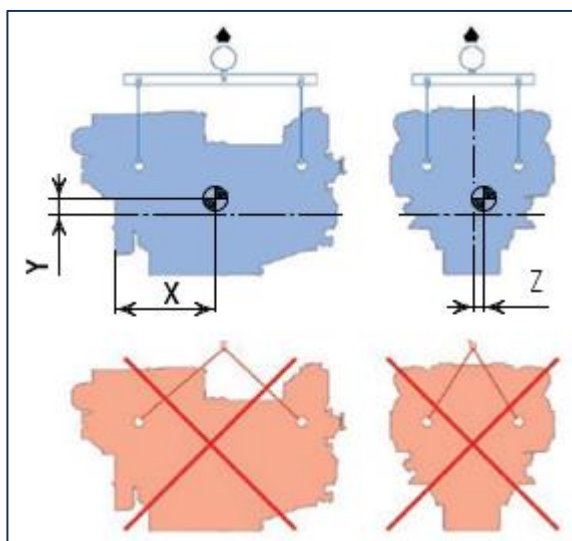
А – Строповка двигателя и положение центра тяжести (ц.т.) двигателя
